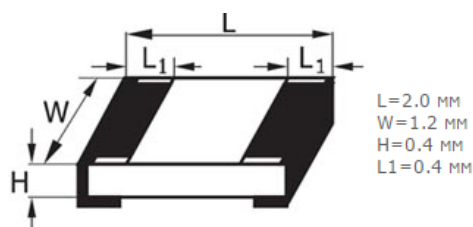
Керамічний конденсатор типорозміру 0805
